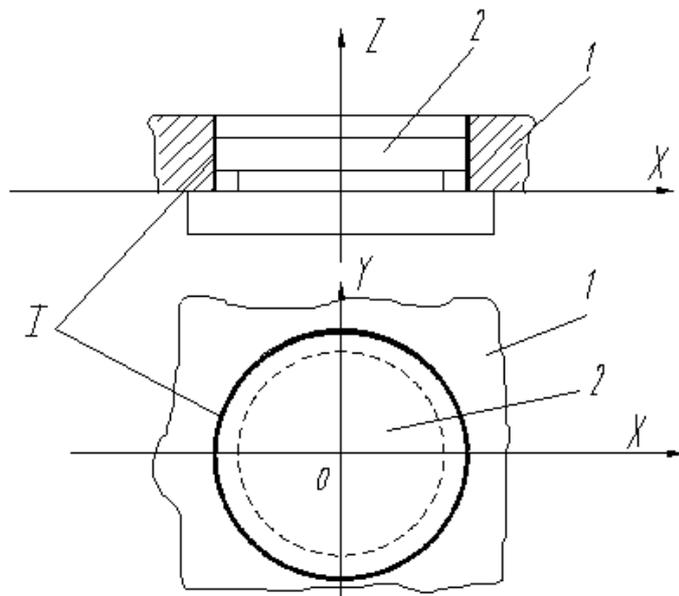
Двойная опорная база. *I* - двойная опорная база заготовки, лишаящая ее перемещений вдоль осей *X* и *Y*; *1* - заготовка; *2* - элемент приспособления
